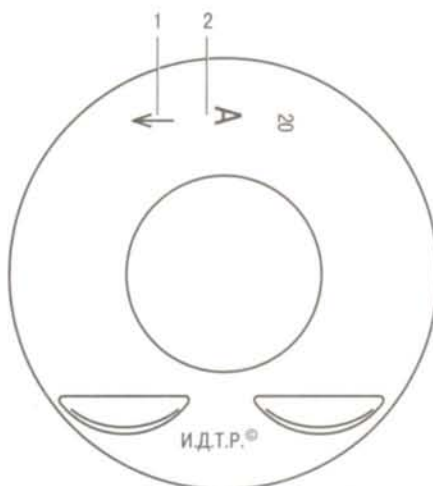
Маркировка поршня: 1 – указатель передней части двигателя; 2 – класс поршня
